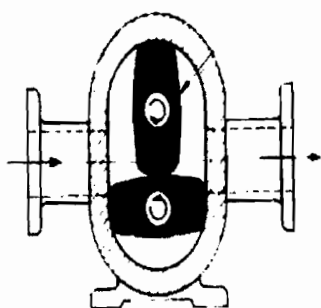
เครื่องสูบลมแบบเฟืองภายใน Internal Gear Pump
